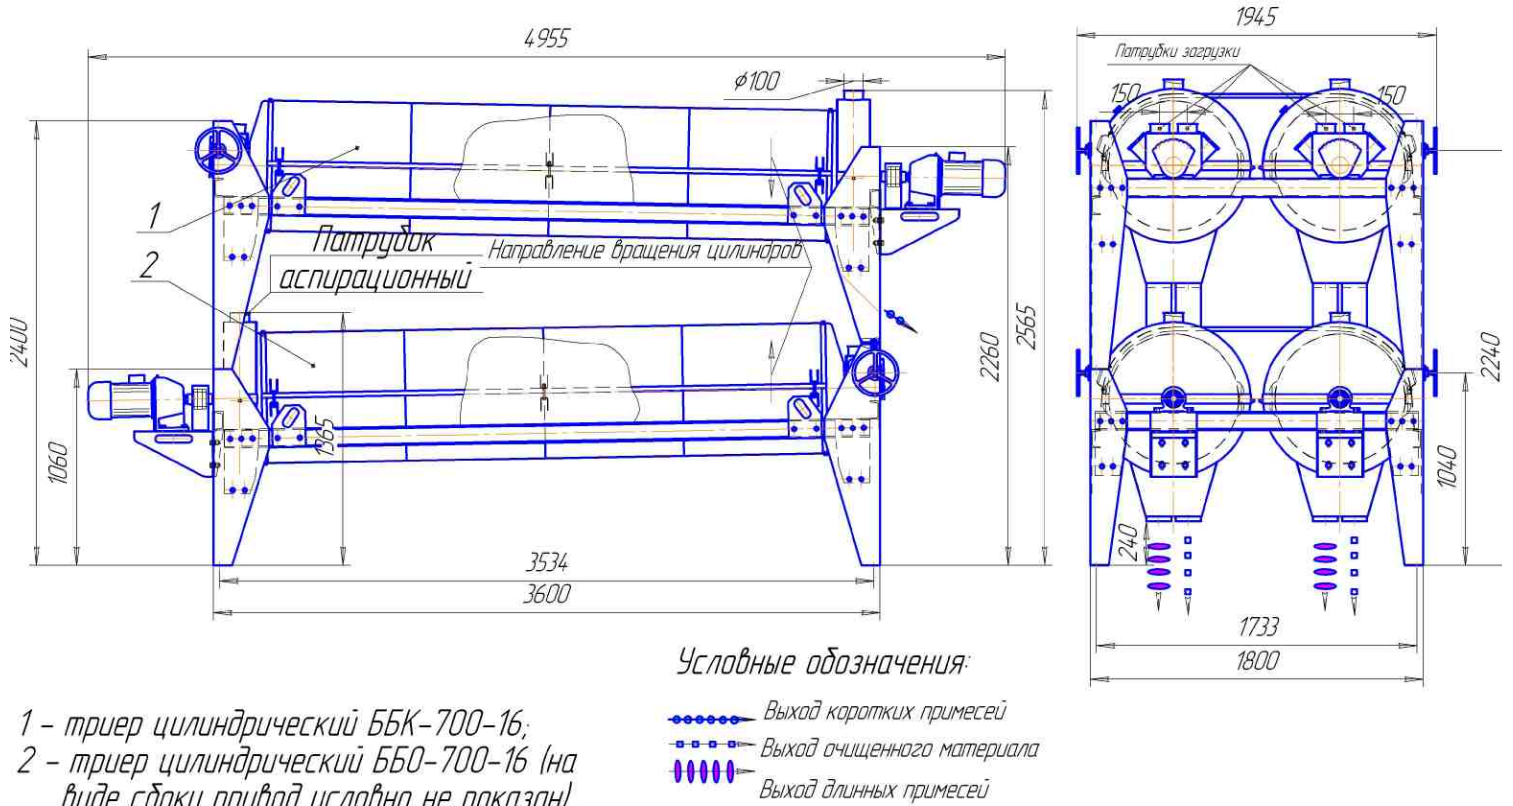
Габаритные, установочные и присоединительные размеры блока триерного P1-ББТ-700-16
